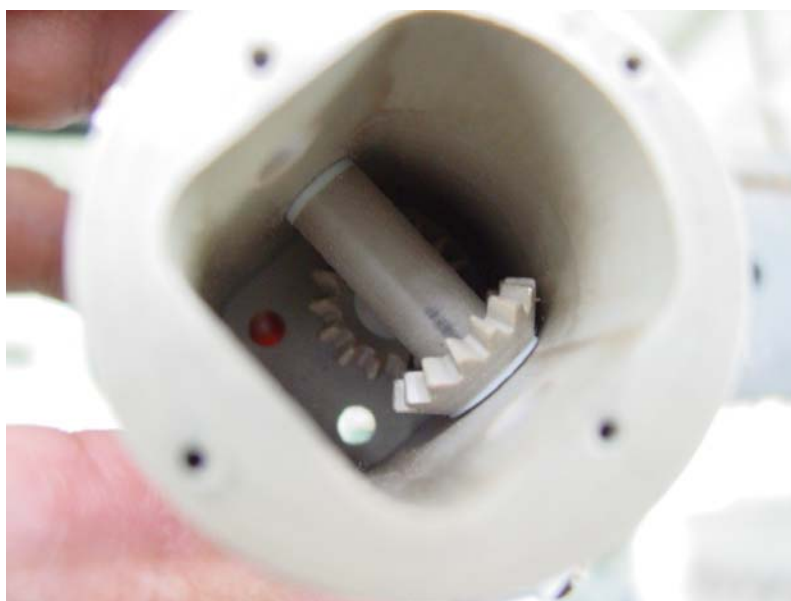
Vista inferior do dispositivo de tracção onde é visível o eixo horizontal e as engrenagens cónicas que consistiam a transmissão do movimento do motor ao dispositivo. A rotação do eixo horizontal fazia girar as amarras que iam enrolando o provete, estirando desse modo o material.
